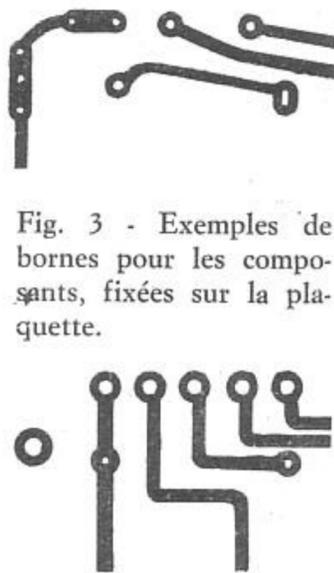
Exemples de bornes pour les composants, fixées sur la plaque.
